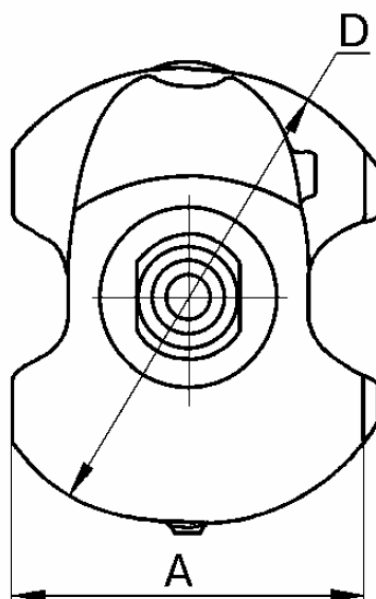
Размеры противовесов коленчатых валов 2108/21081
